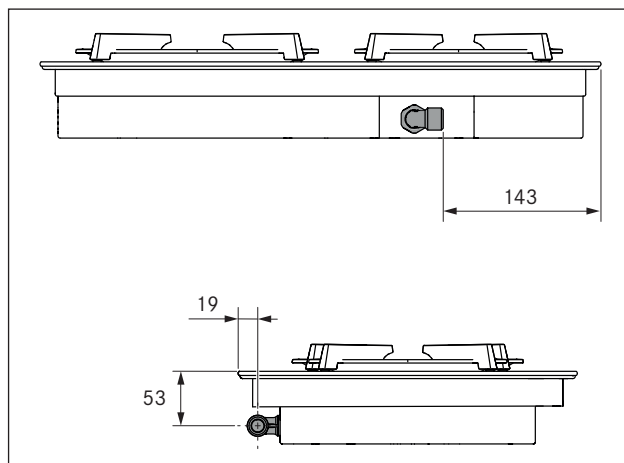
Zijdelingse uitsparing voor de gasaansluiting (vooraanzicht)
